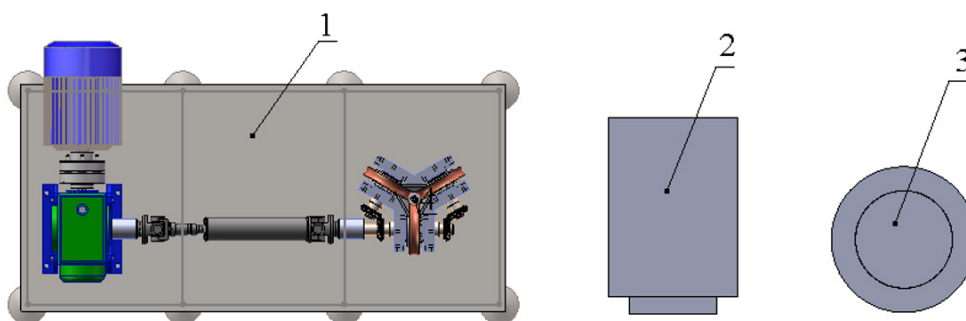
Схема розташування установки валкової розливки-прокатки і допоміжного обладнання
